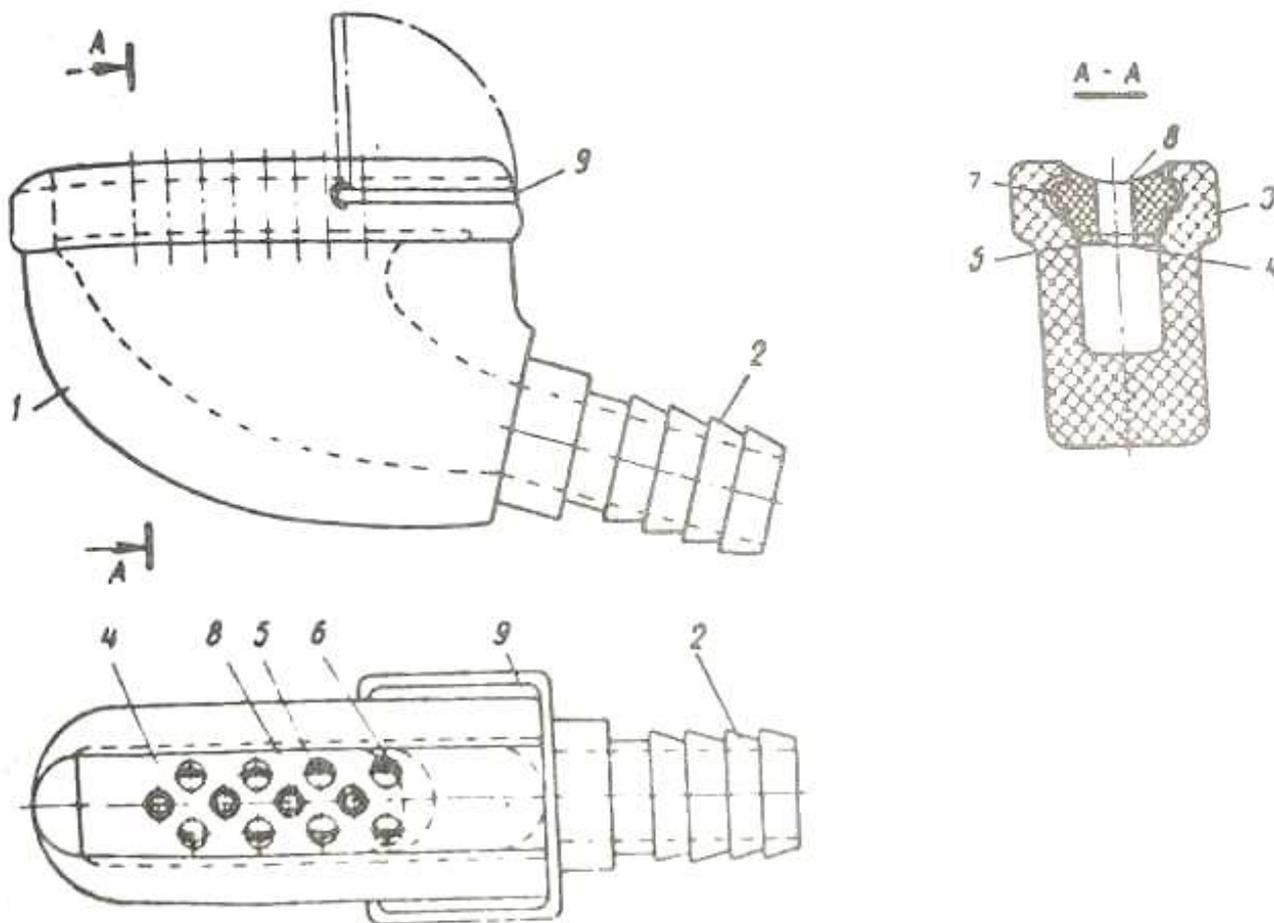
Схема пневматической насадки для съема ягод облепихи
